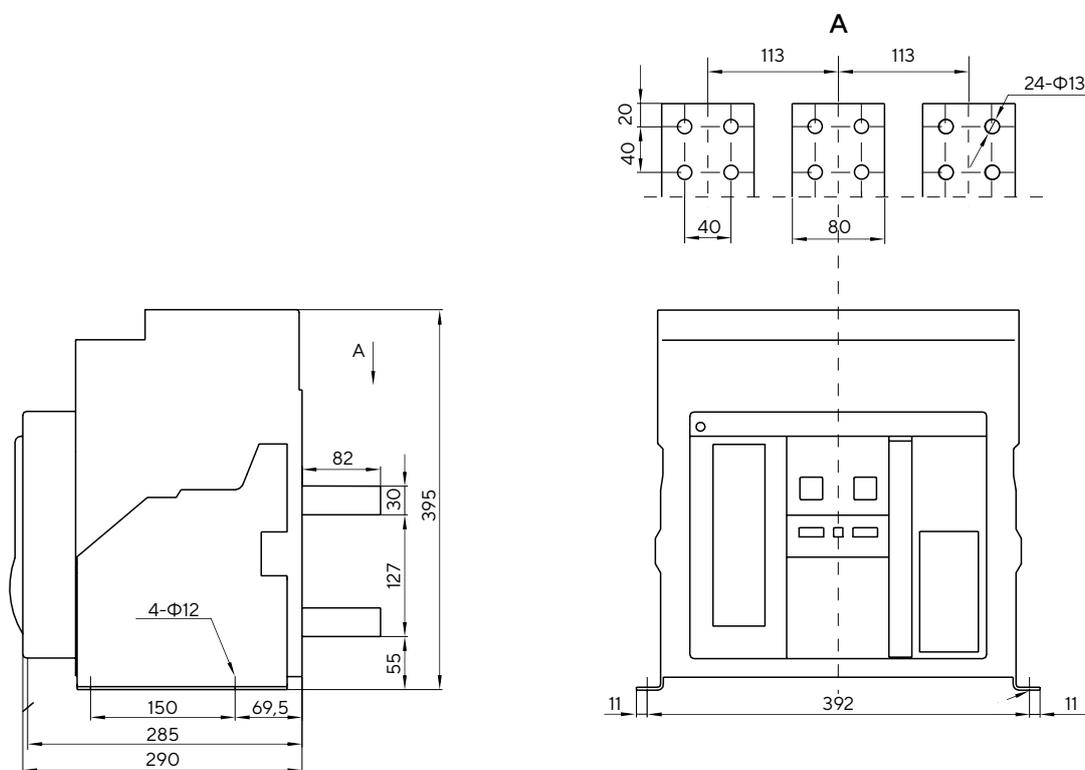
Габаритные размеры стационарных трехполюсных выключателей типоразмера Е
